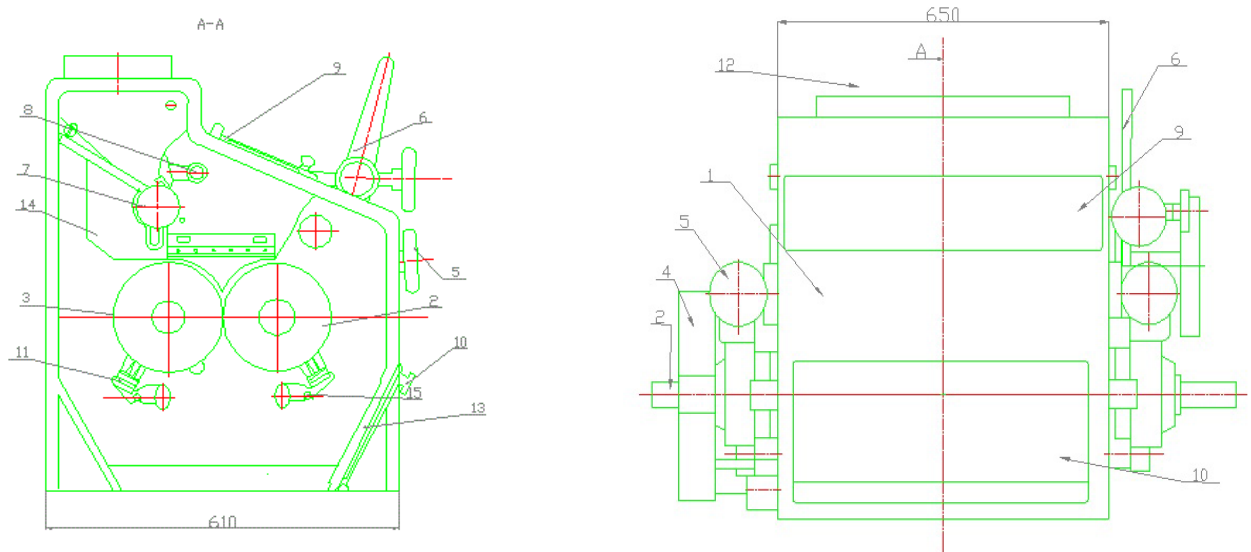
Вальцювий верстат марки Р6-ВС: 1 – станина; 2 – швидкообертовий валець; 3 – повільнообертовий валець; 4 – міжвальцюва передача; 5 – механізм налаштування вальців на паралельність; 6 – притисно-відкидний механізм; 7 – живильний валець; 8 – механізм регулювання подачі; 9 – верхня дверка; 10 – нижня дверка; 11 – щітка; 12 – живильна труба; 13 – заслінка; 14 – накладка; 15 – вісь.
